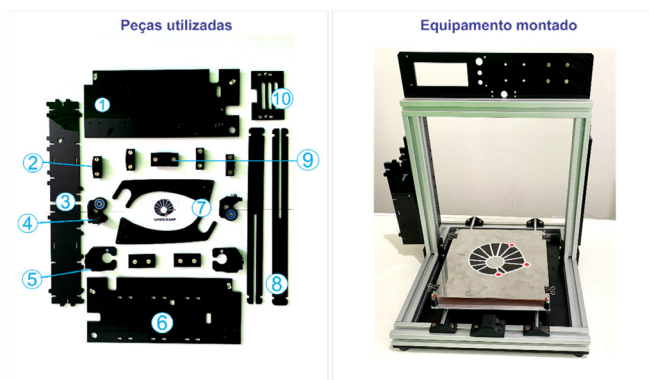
Montagem de painel e laterais: (1) tampa superior, (2) fixação de motor de extrusão, (3) painel lateral da caixa de componentes eletrônicos, (4) roldana para movimento dos eixos, (5) trava superior da barra roscada, (6) tampa inferior, (7) suporte para rolo de filamento, (8) fixação do rolo de filamento, (9) junção do tensor de correia (belt idler), (10) tampa para cooler de resfriamento da placa controladora
